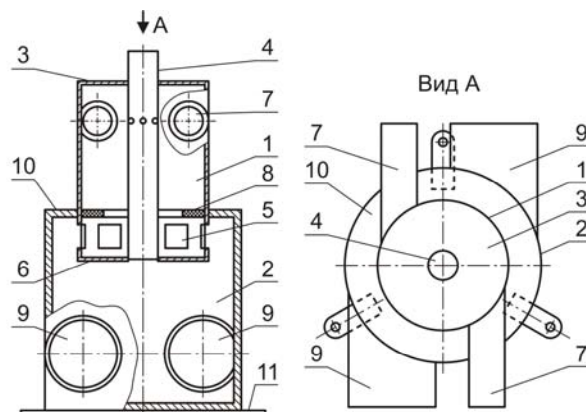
Конструктивная схема деаэратора ДЦВ-670: 1 – корпус; 2 – центробежный сепаратор; 3, 6 – верхняя и нижняя торцевые крышки корпуса соответственно; 4 – трубопровод отвода пара; 5 – окна для отвода воды из корпуса; 7, 9 – подводящие и отводящие тангенциальные патрубки соответственно; 8 – кольцевая перегородка (шайба); 10, 11 – верхняя и нижняя торцевые крышки центробежного сепаратора соответственно
